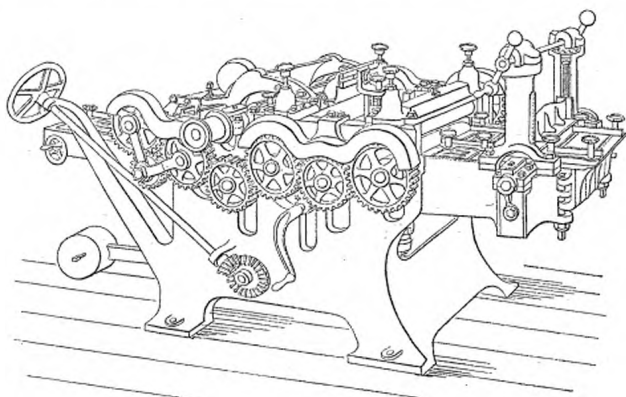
Machine à raboter double des *Indiana Machine Works*.
